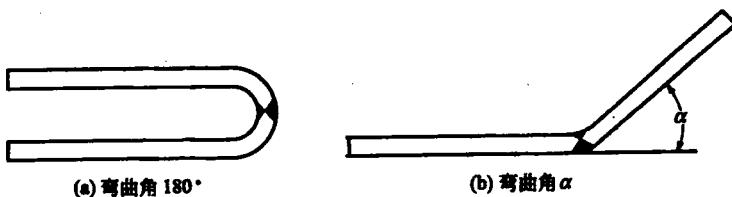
焊缝冷弯曲试验中弯曲角的要求
